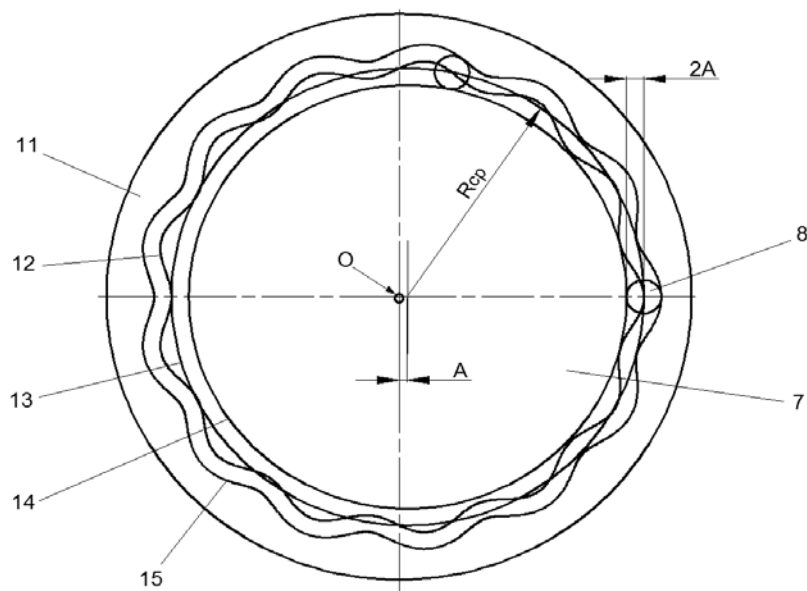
Схема и геометрические параметры деталей зацепления планетарной радиально-плунжерной передачи
